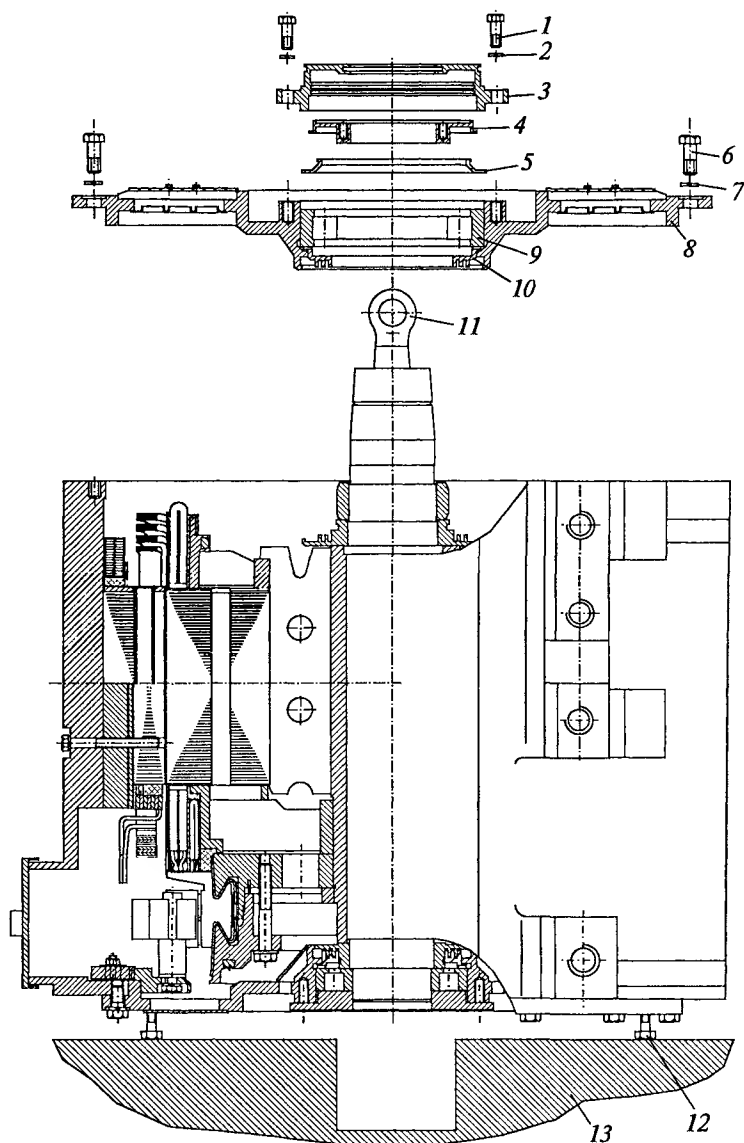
Разборка большого подшипникового щита ДТК-800КЭ:
